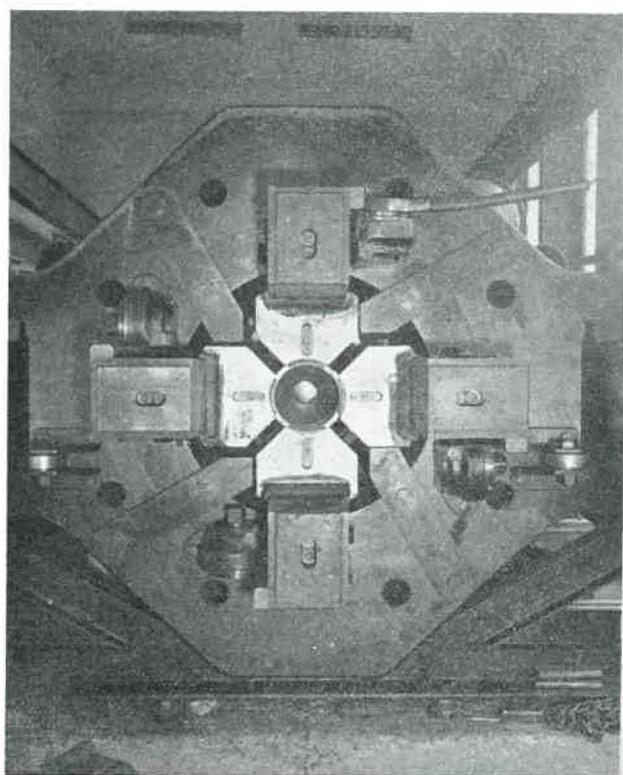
Vue des coins avec leur garniture de fourrures coniques montées sur la machine.
